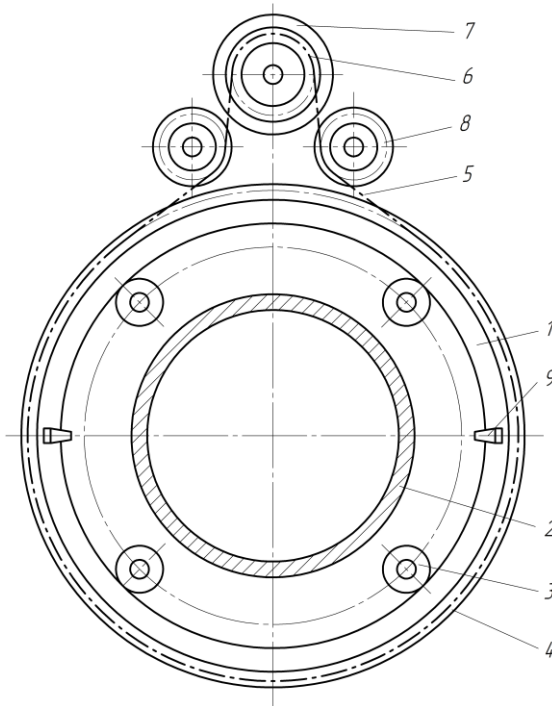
Конструктивна схема робочого органа установки для нанесення поліуретанового покриття.
